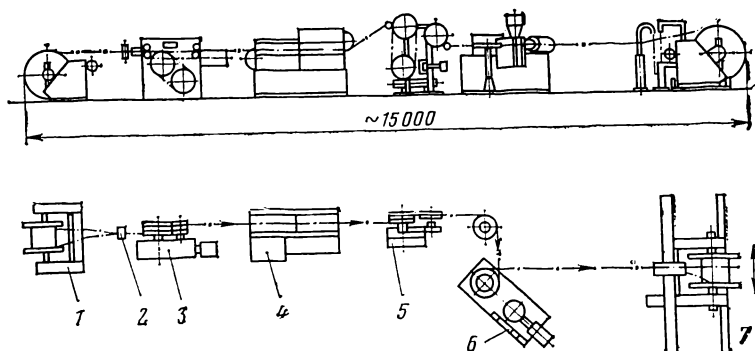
Схема агрегата для одновременной подкалибровки и очистки медной проволоки и непрерывной отливки на ней полиэтиленовых шайб.
